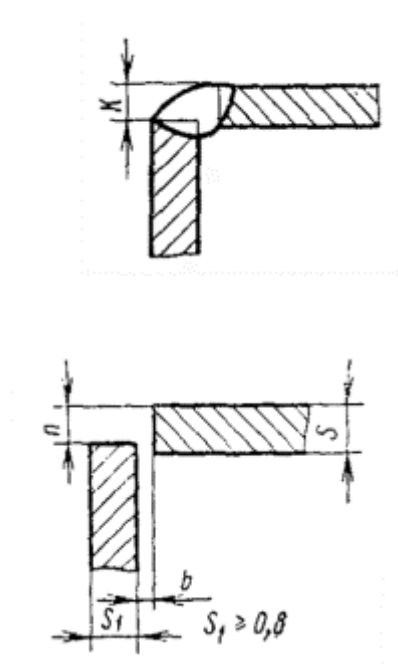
Сварное соединение по ГОСТ14771-79-У4
